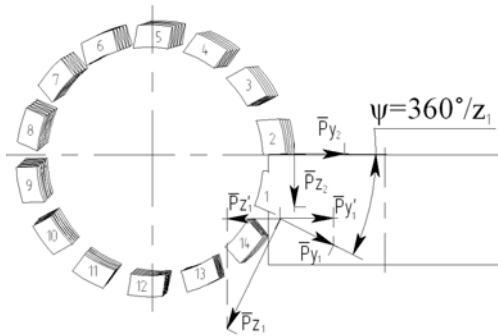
Схема расположения сил  $P_z$  и  $P_y$  на фрезе ( $\psi$  – угловой шаг зубьев фрезы)
